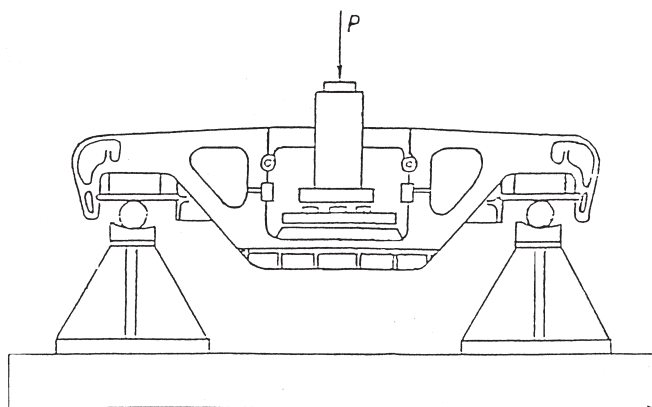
Схема усталостных стендовых испытаний ГосНИИВ-ВНИИЖТ
